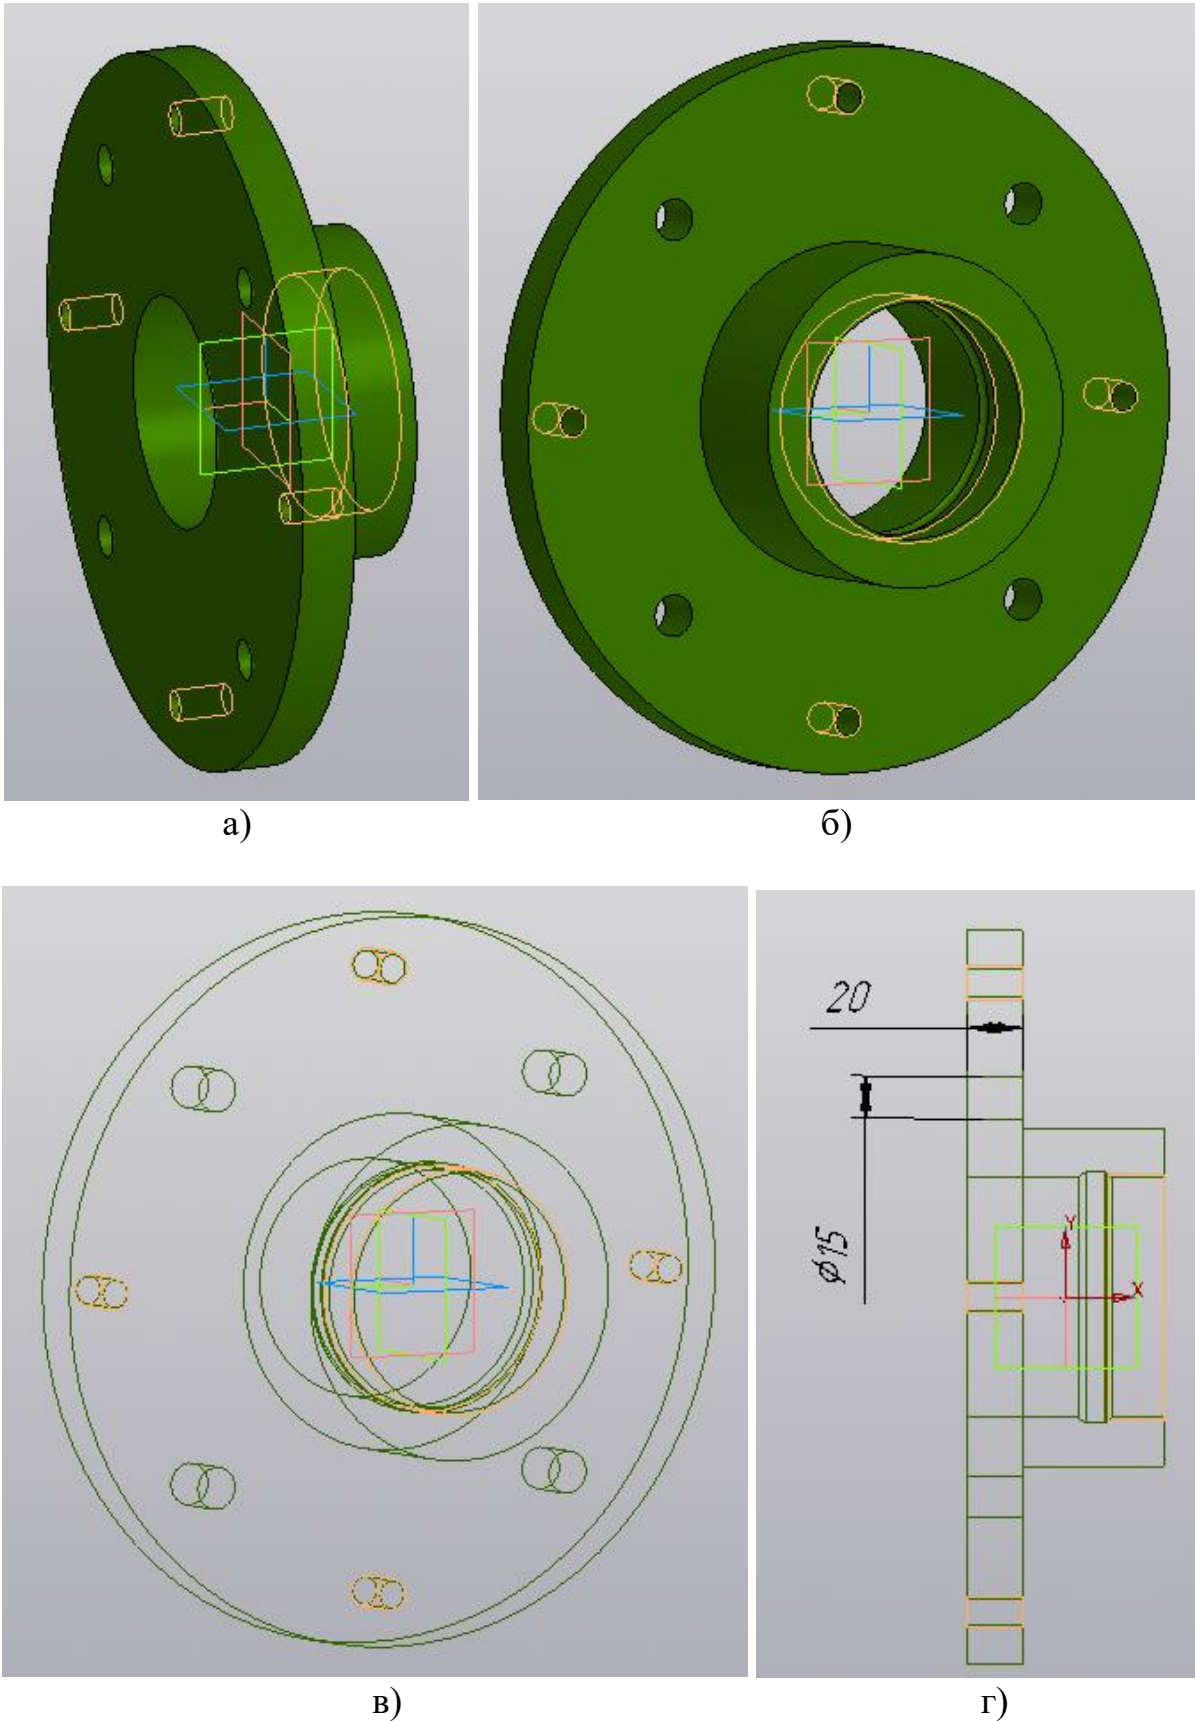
(а, б, в) 3д модель заготовки після операції свердління отворів
